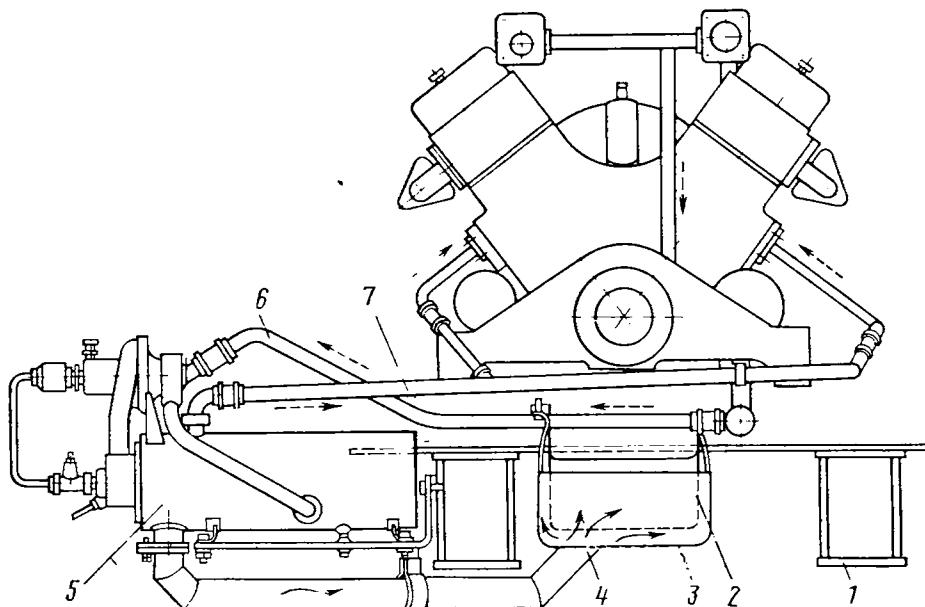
Установка пускового подогревателя двигателя на автомобиле БелАЗ-540А:
